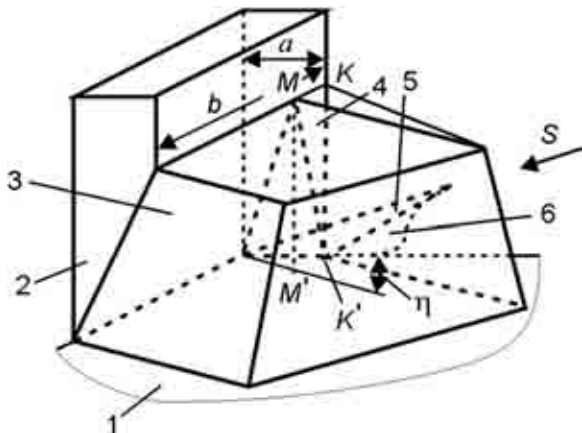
Схема удаления припуска: 1 — резец; 2 — припуск; 3 — стружка; 4 — выдавливаемая часть припуска; 5 — расчетная неровность; 6 — выдавленная часть неровности
